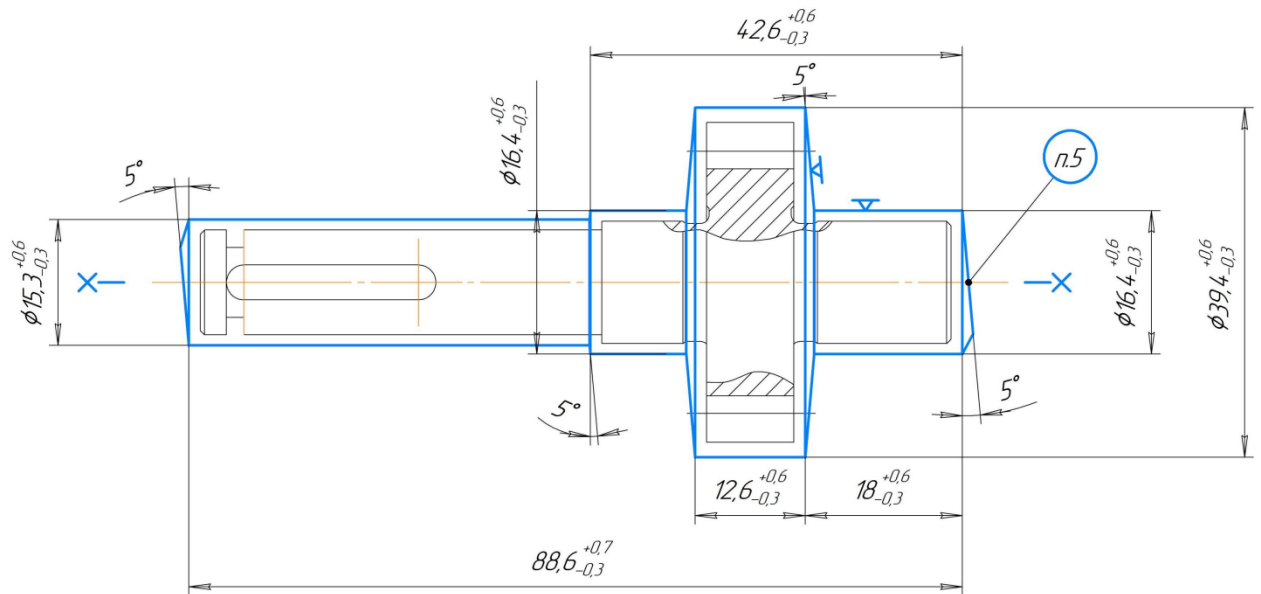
Ескіз заготовки деталі 14.01.05
